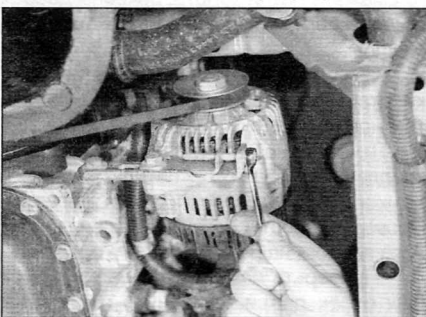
, а. Поверните регулировочный болт, чтобы снять натяжение с приводного ремня...
